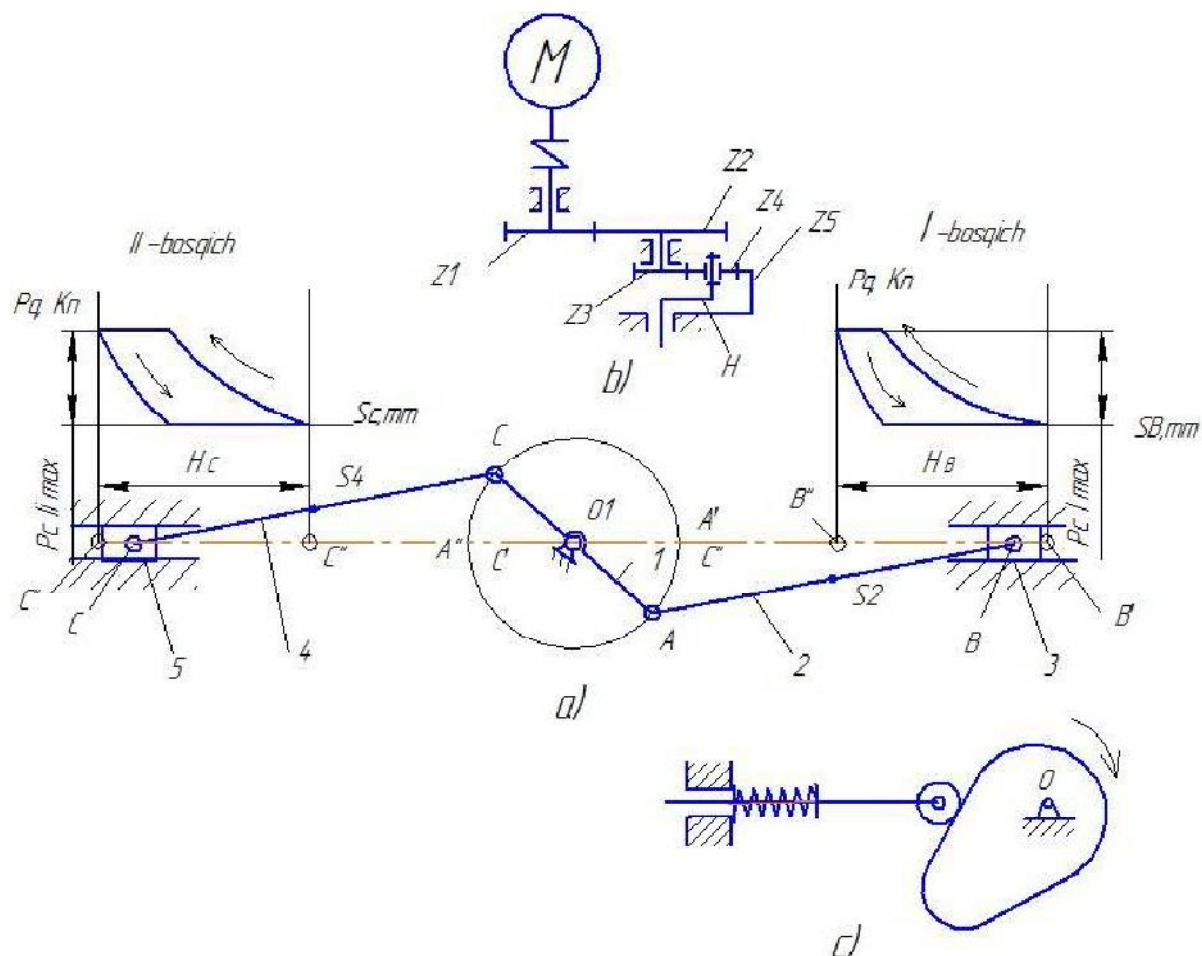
Кинематическая схема двухступенчатого двухцилиндрового поршневого компрессора
